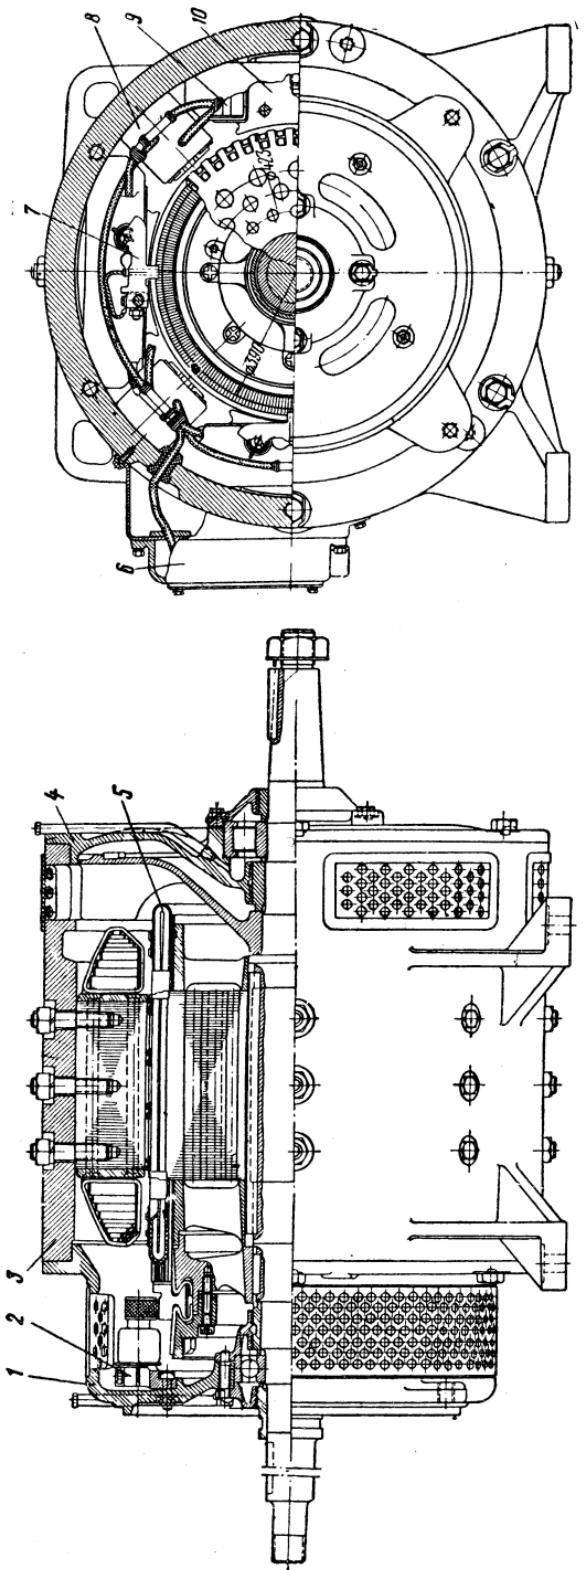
Продольный и поперечный разрезы двигателя НБ-430А:
